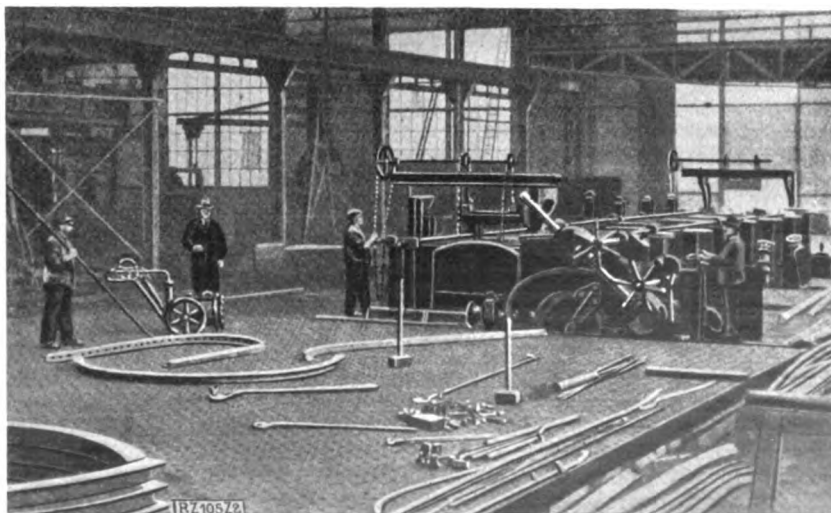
Spantenplan einer Werft mit Glühofen, Schmiegemaschine und Spantbiegemaschine.
